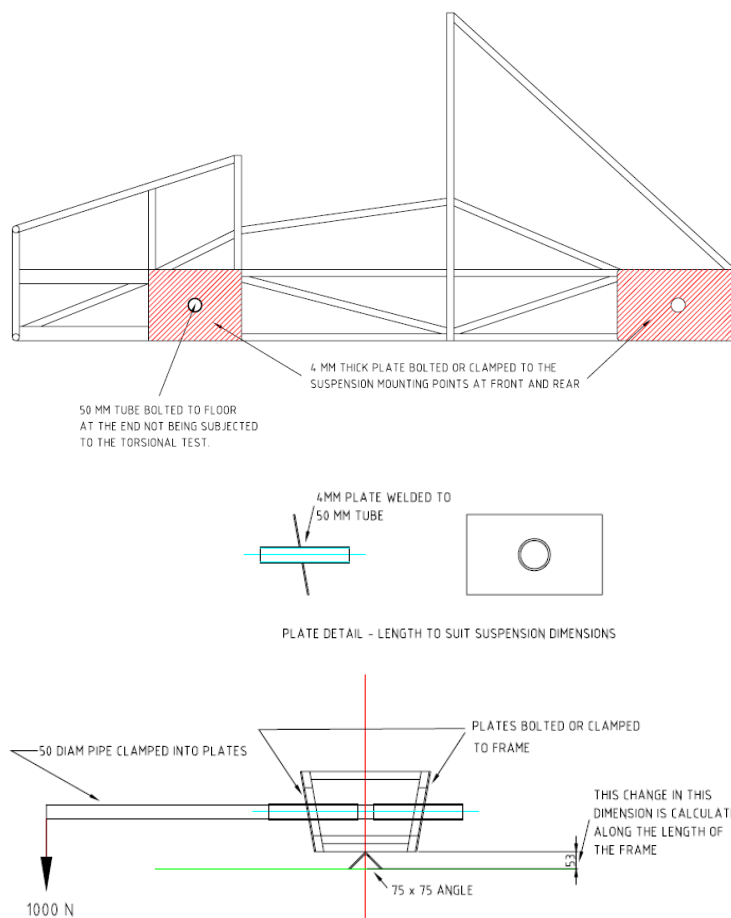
Aplicação de chapas nos apoios da suspensão (O’Neill, 2005).
